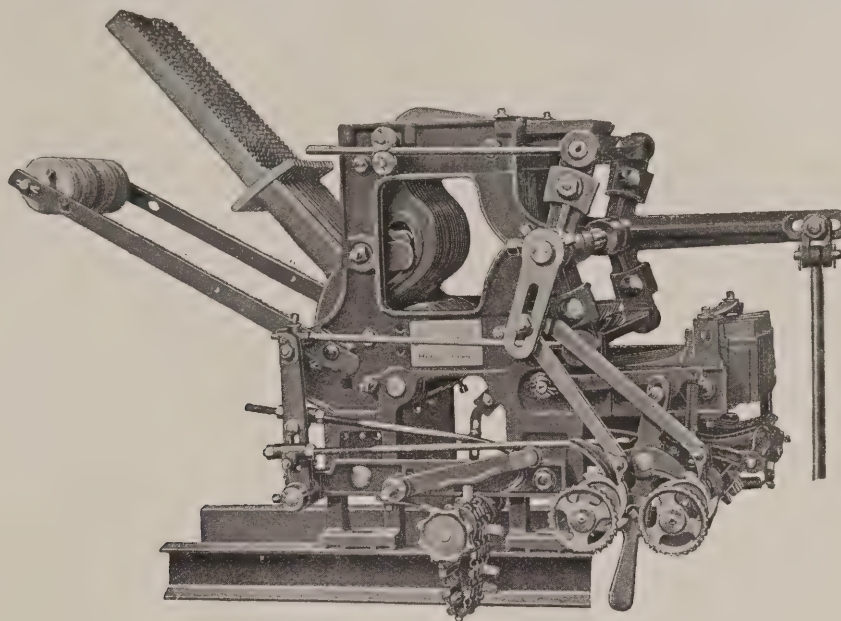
Schaubild der Zweizylinderschaftmaschine
